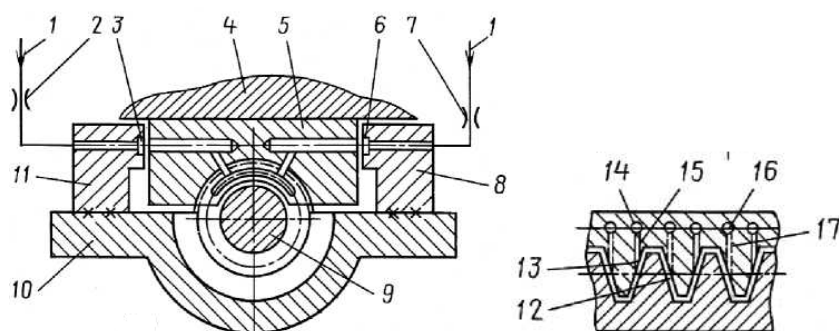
Конструкция гидростатической червячно-реечной передачи
